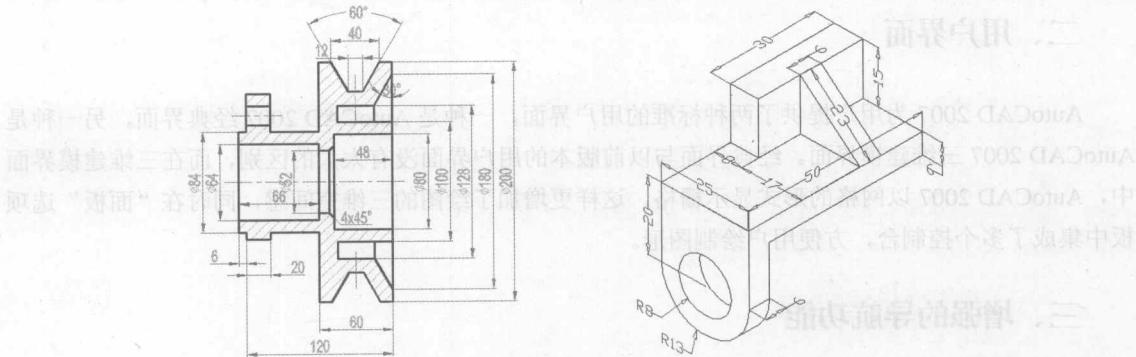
利用 AutoCAD 标注的平面图形和三维图形
